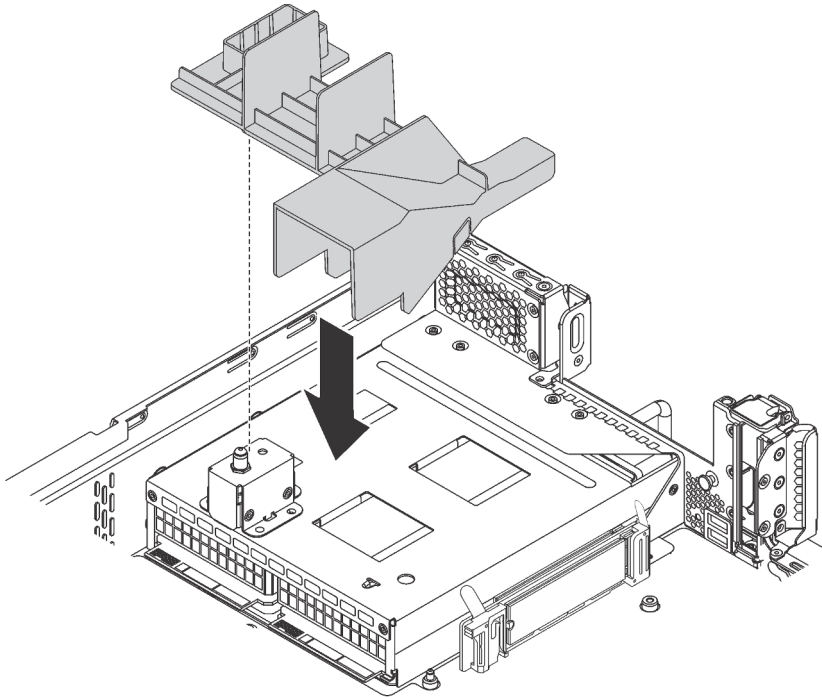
Installation der Luftführung für das M.2-Laufwerk
